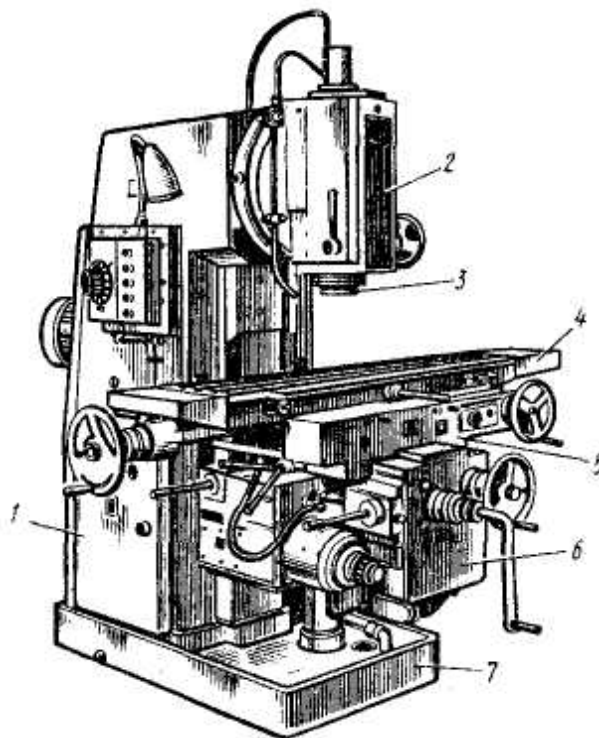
Вертикально-фрезерный станок: 1 – станина; 2 – шпиндельная головка; 3 – шпиндель; 4 – стол; 5 – каретка; 6 – консоль; 7 – фундаментная плита
